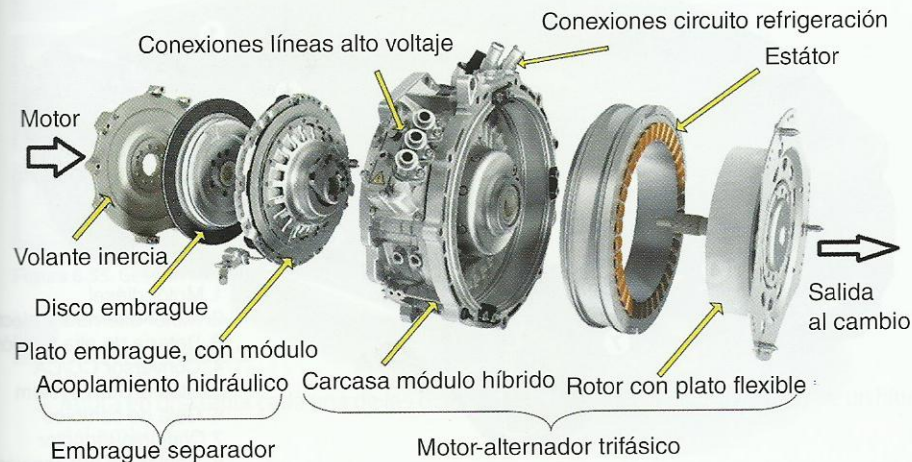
Embrague separador y motor-alternador (fuente Porsche).
